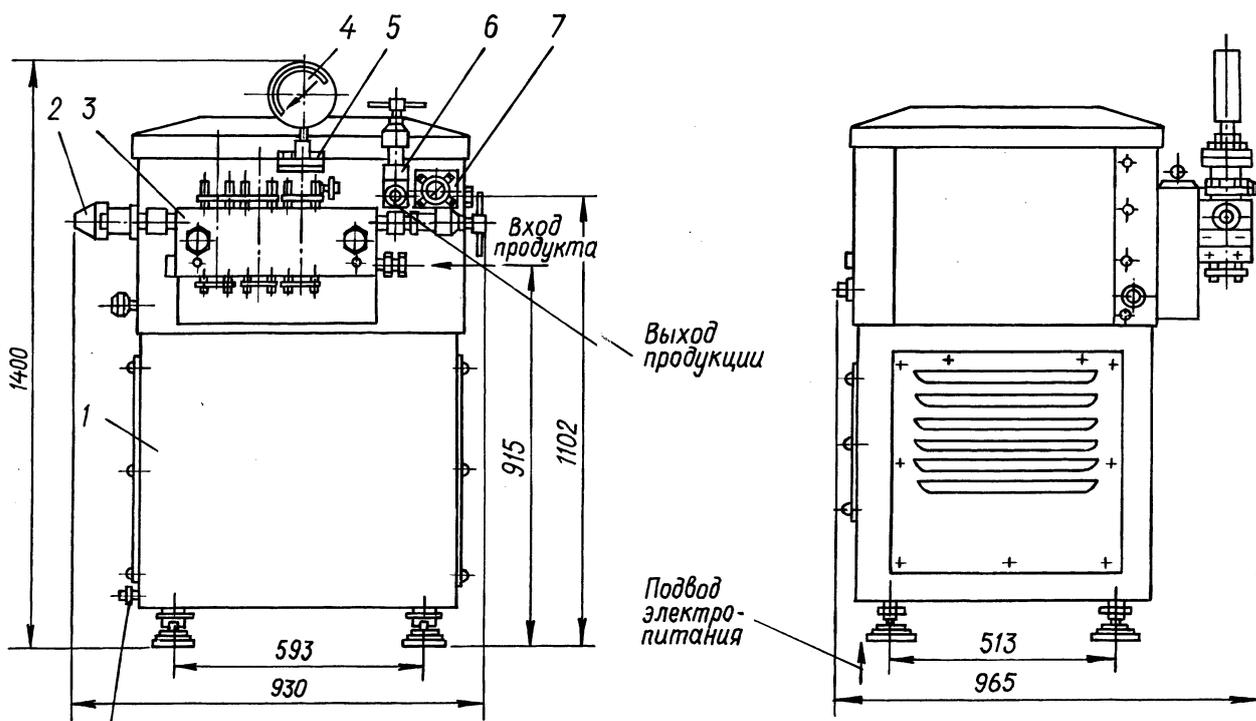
Габаритный чертеж гомогенизатора марки К5-ОГА-1,2: 1 – станина; 2 – предохранительный клапан; 3 – плунжерный блок; 4 – манометр; 5 – манометрическая головка; 6 – гомогенизирующая головка; 7 - амперметр
